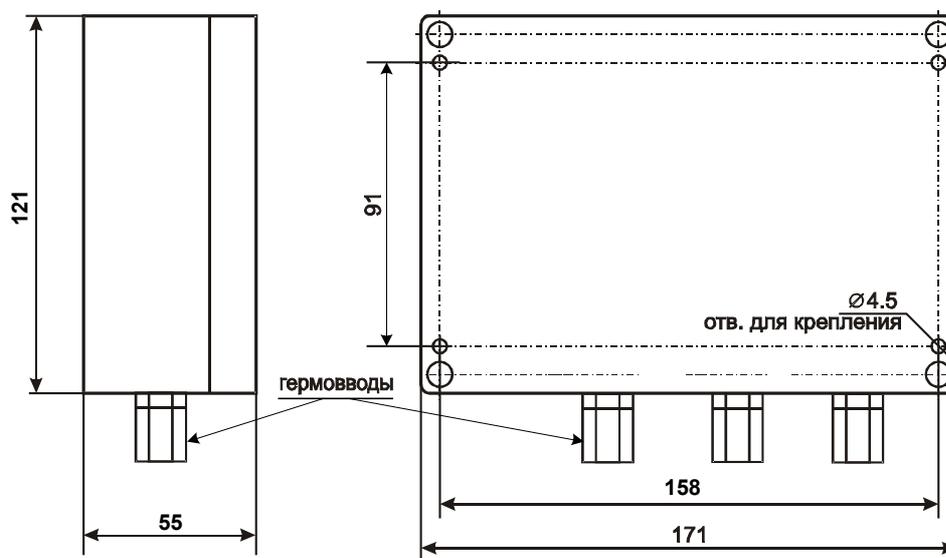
Внешний вид и габаритные размеры ПИ-01 в исп. IP 65
